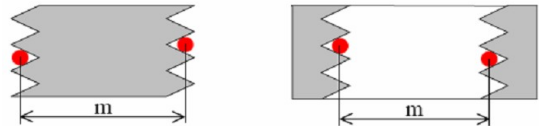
Внешняя резьба с проволочками и внутренняя резьба с шариками
